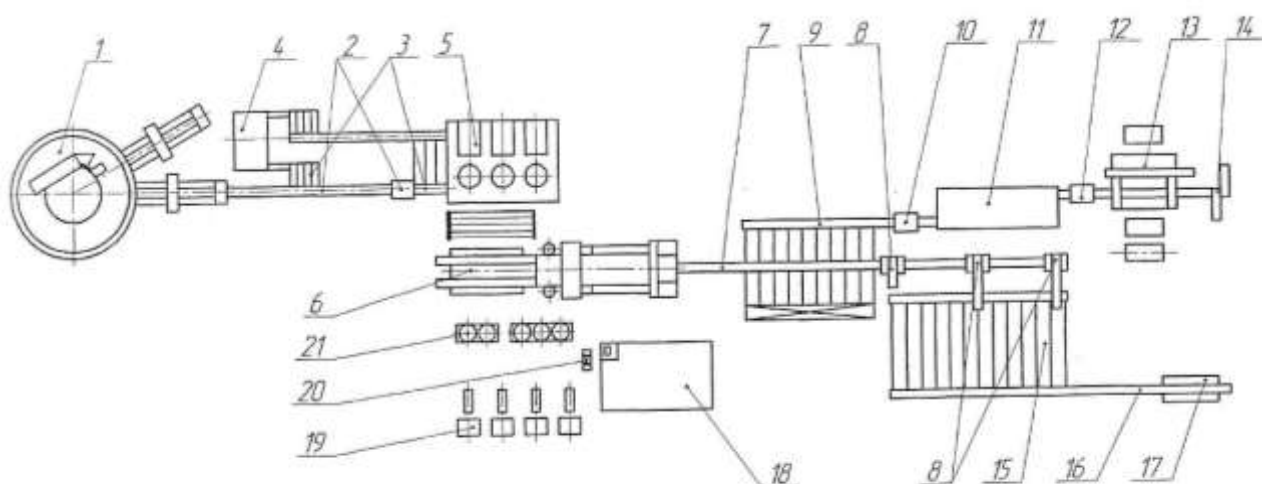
план расположения оборудования прессовой установки на участке горячей деформации [25] 1- газовая нагревательная печь; 2 – установка для гидросбива окалины; 3 – механизм нанесения смазки; 4 – прошивной пресс; 5 – подогревательные индукционные печи; 6 – трубопрофильный пресс; 7 – выходной рольганг трубного пресса; 8 – пила горячей резки, 9 – выходной рольганг подогревательной печи; 10 – установка для гидросбива окалины и смазки; 11 – газовая подогревательная печь; 12 – механизм для снятия окалины и смазки с наружной поверхности труб; 13 – редукционный стан; 14- летучая пила; 15 – охлаждающий стол; 16 – отводящий рольганг; 17 – установки для дробеструйной отчистки наружной поверхности труб; 18 – машинный зал; 19 – водяные насосы; 20 – воздушные компрессоры; 21 – воздушно-гидравлические аккумуляторы
